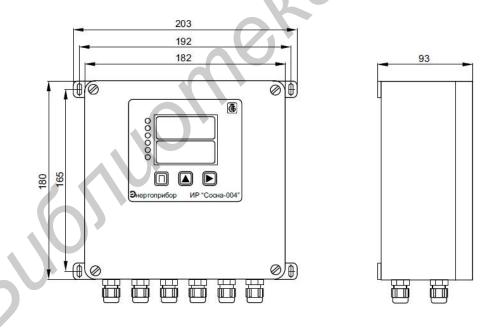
Габаритно-установочные размеры ИР «Сосна-004»
